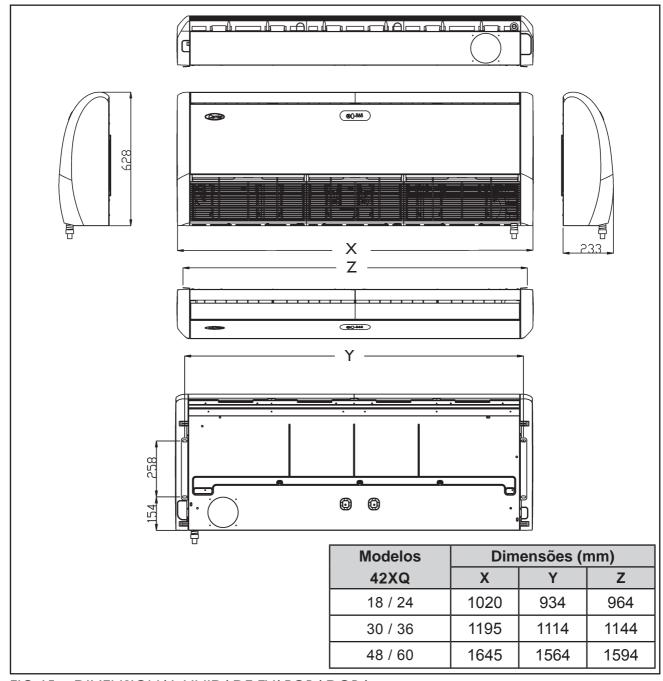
DIMENSIONAL UNIDADE EVAPORADORA
